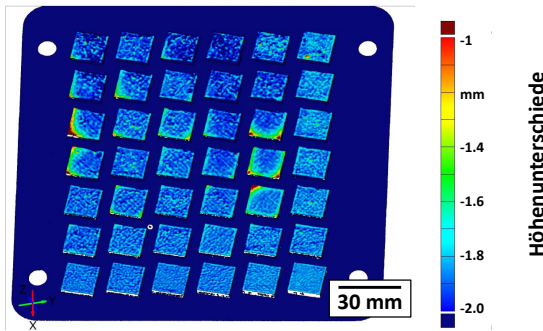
3D-Scan einer Bauplattform mit Testkörpern mit Übergangsbereich in den Schichten nach dem Aufbau von Stützstrukturen [S13].
